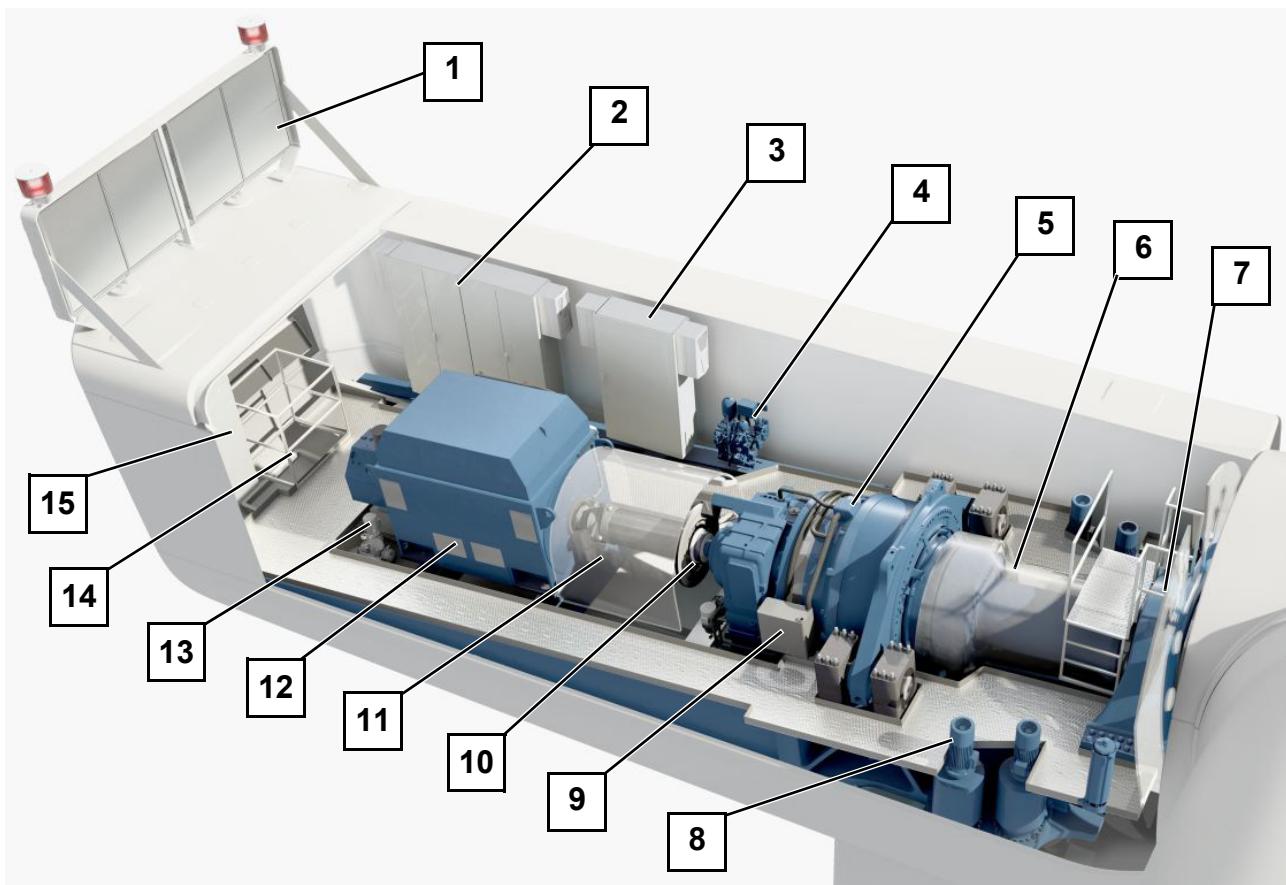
Übersichtszeichnung Maschinenhaus
